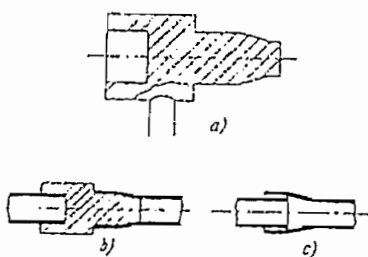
Manguito de soldar calentado eléctricamente. a) El elemento de calentamiento combinado se calienta por medio de una lámpara o soplete para soldar; b) se funden las extremidades de los tubos; c) se acoplan.
